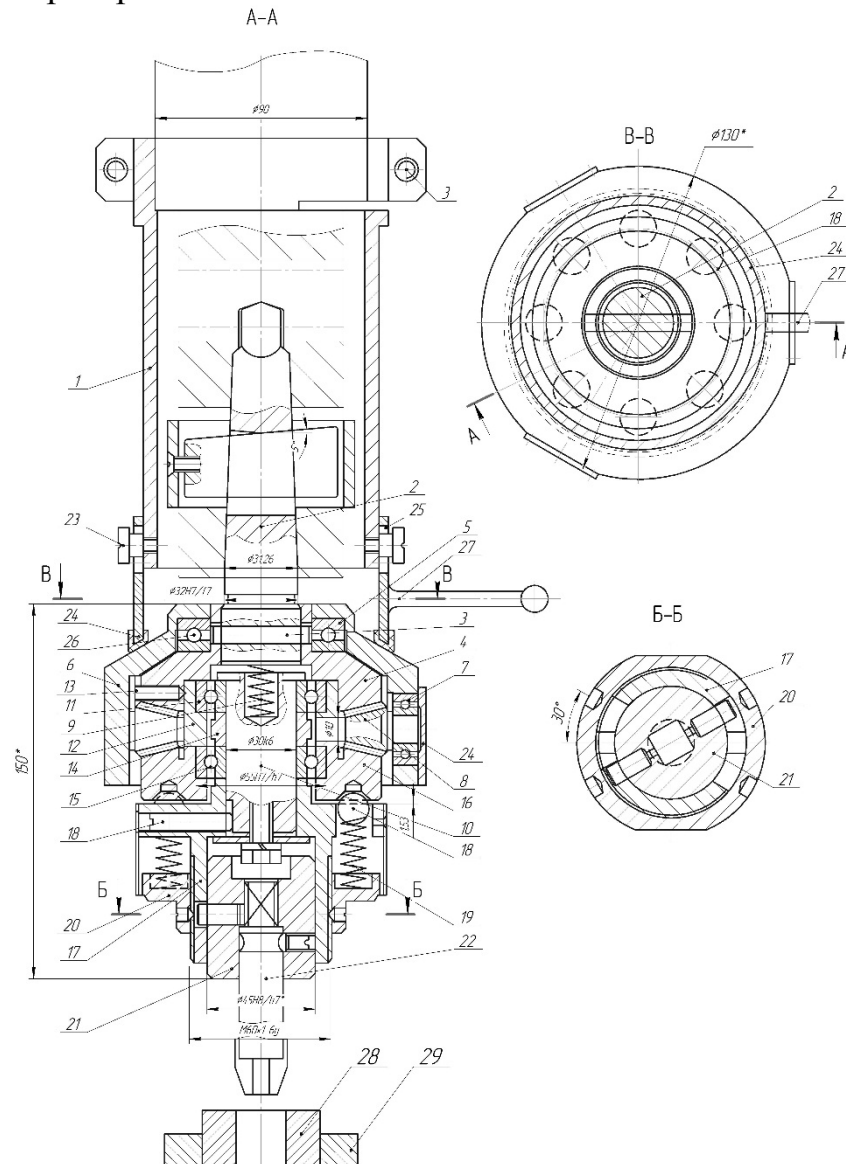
Реверсивний пристрій для нарізання гайок
